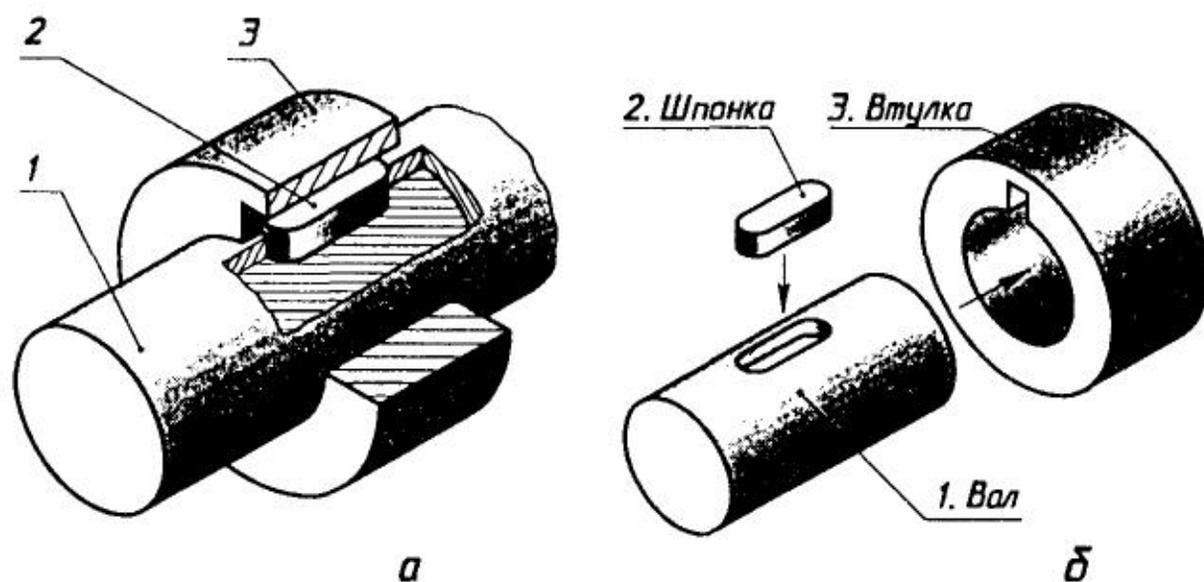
Шпонкове з'єднання: а — загальний вигляд; б — деталі.
